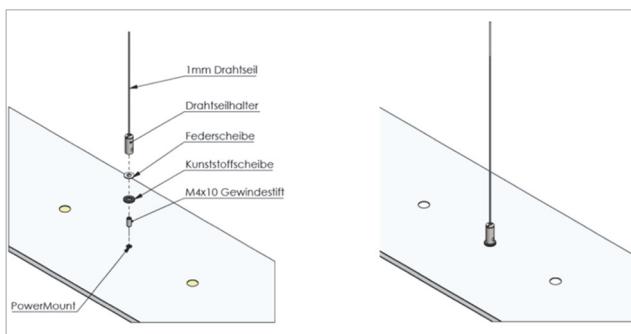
Montagehinweis der Drahtseilhalter an der Leuchte
